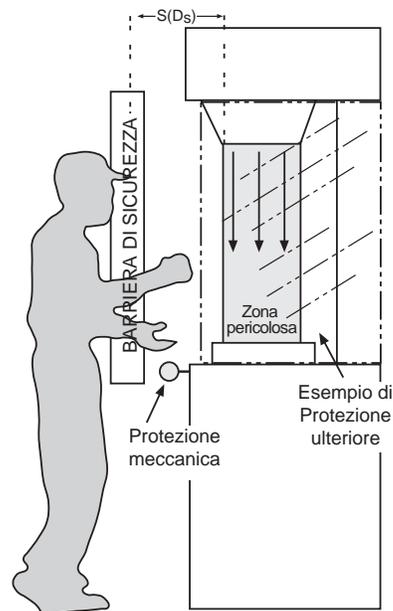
Esempio di installazione corretta della barriera di sicurezza
